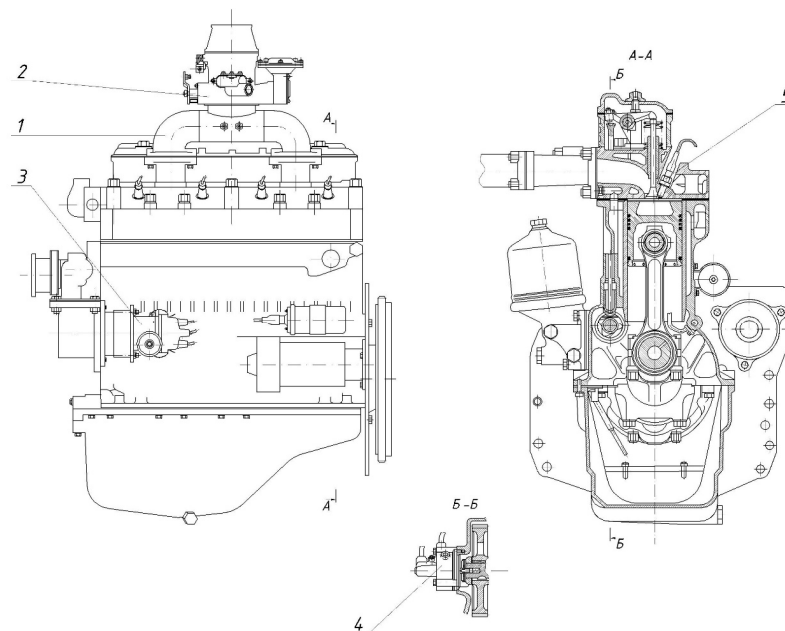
Конвертований з дизеля газовий двигун: 1 – впускний трубопровід; 2 – газоповітряний змішувач; 3 – переривач-розподільник запалювання; 4 – відцентровий датчик обмежувача максимальних обертів колінчастого вала; 5 – свічка запалювання
